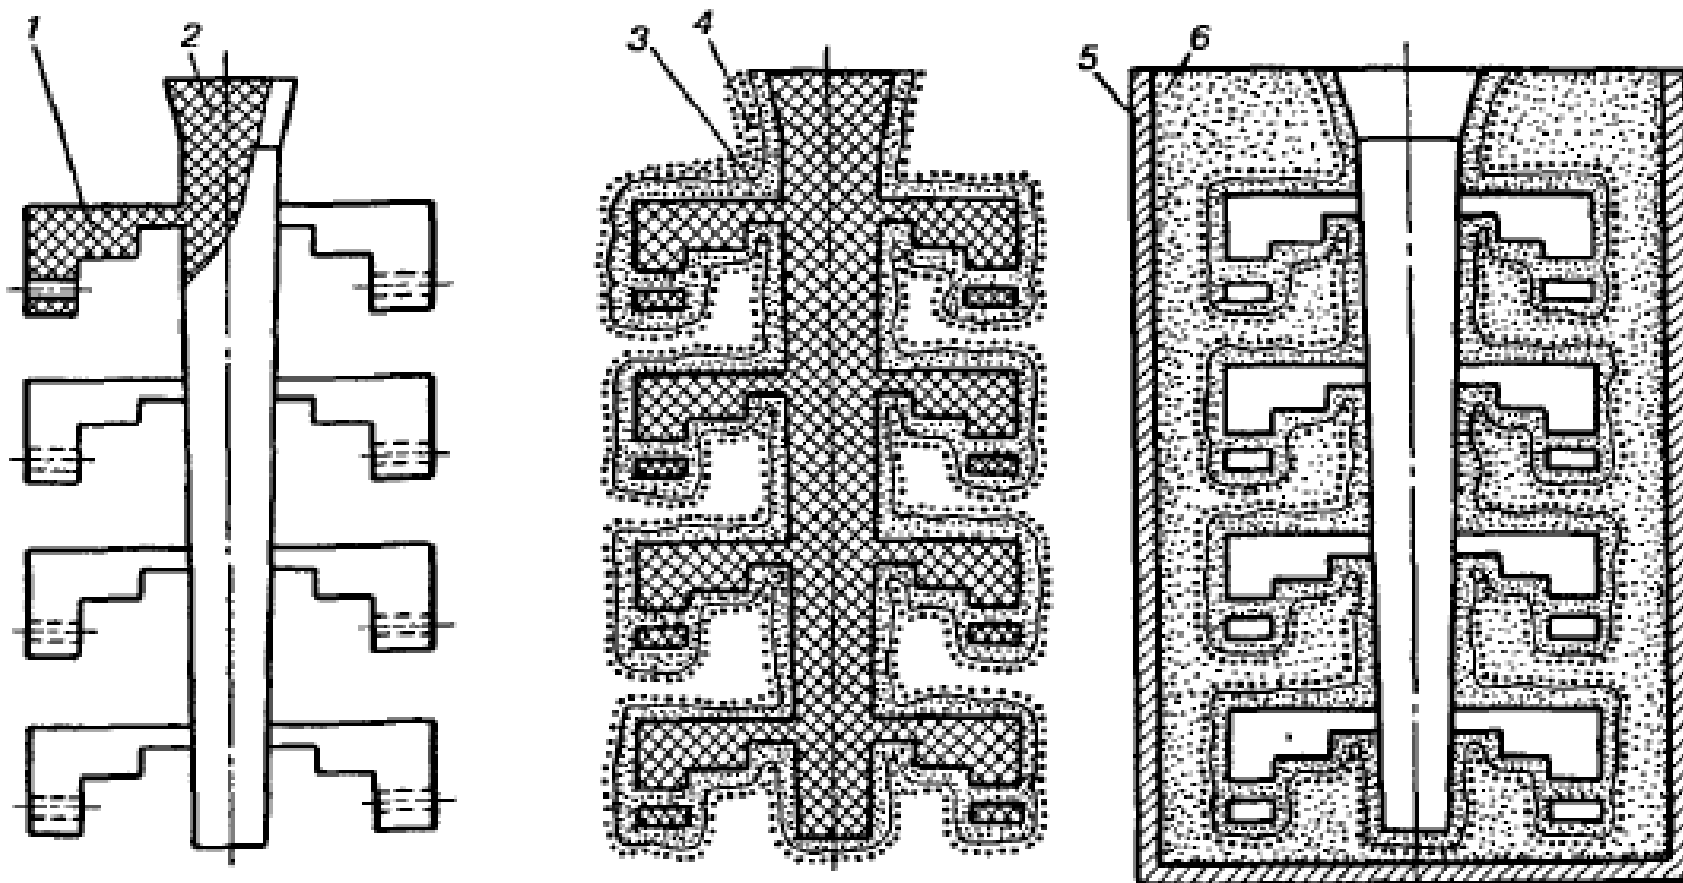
Схеми виготовлення форми за витоплюваними моделями
